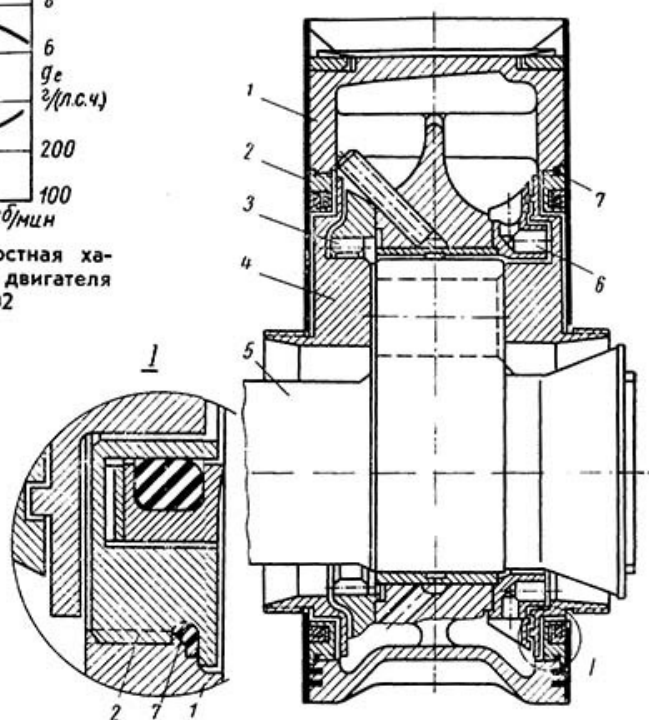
Ротор двигателя ККМ-502 в сборе с эксцентриковым валом:
